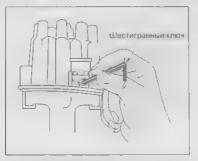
39 Регулировка контактов прерывателя через регулировочное отверстие
